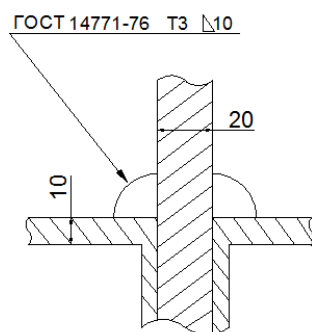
Схема сварного соединения ТЗ по ГОСТ 5264-80 [12]
